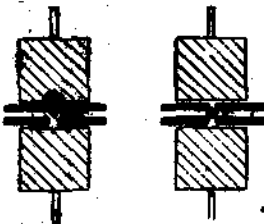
Более простой способ клепки при помощи аппарата для точечной сварки.
